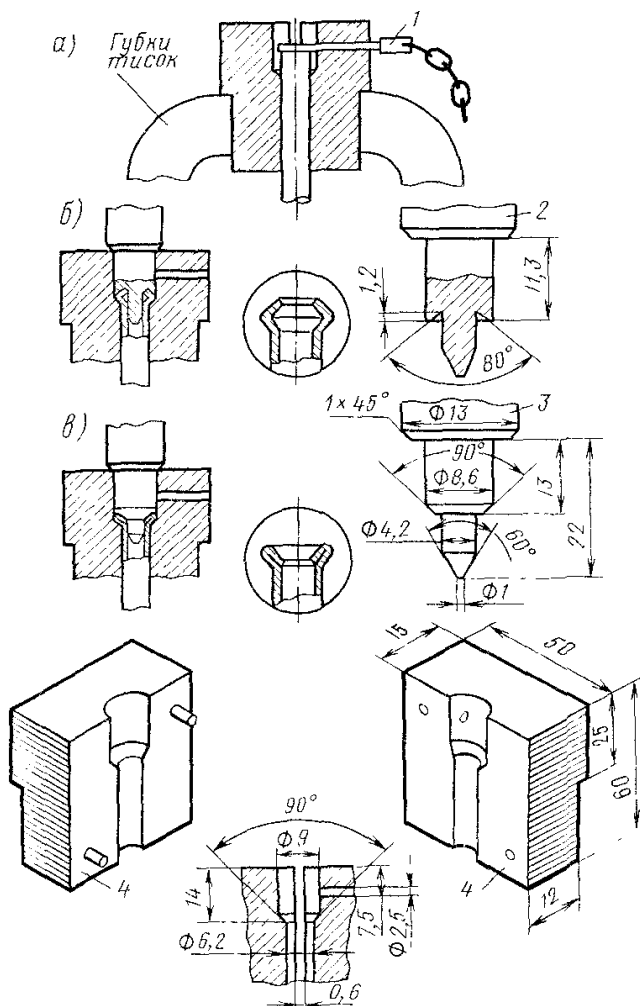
Двойная развальцовка трубок гидропривода тормозов:
